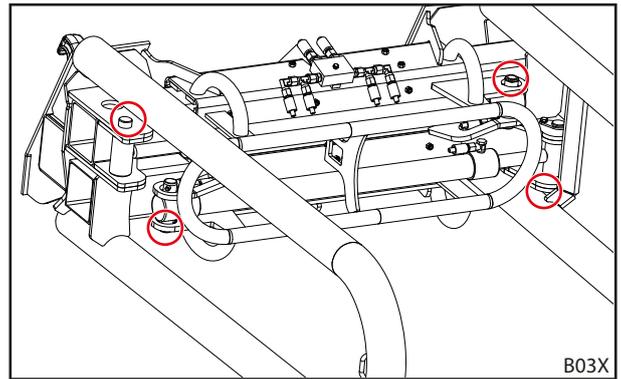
Puntos de engrase de la pinza para pacas encintadas Pro H
